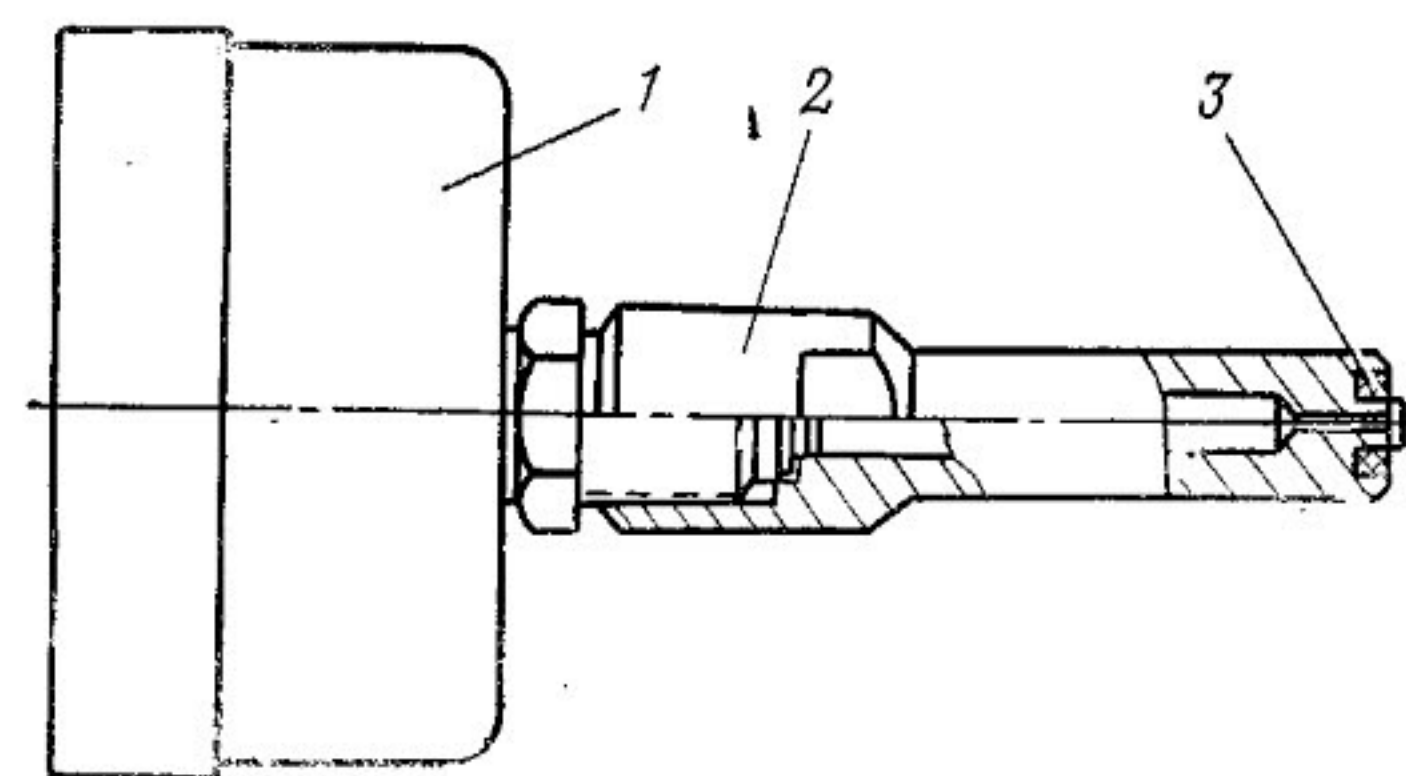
Прибор для проверки давления в камерах авиаколес:
